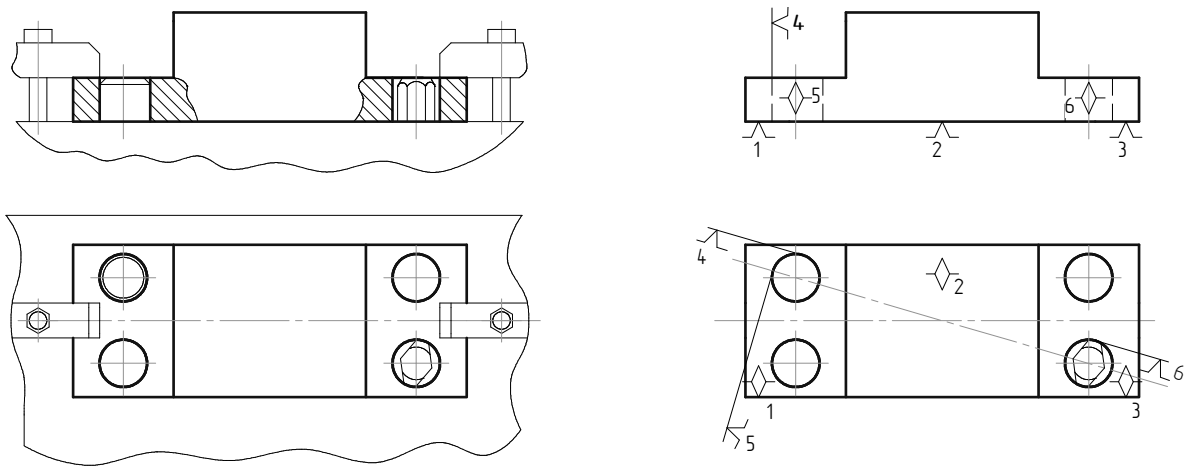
Схема базування корпусної деталі по площині і двох отворах.
